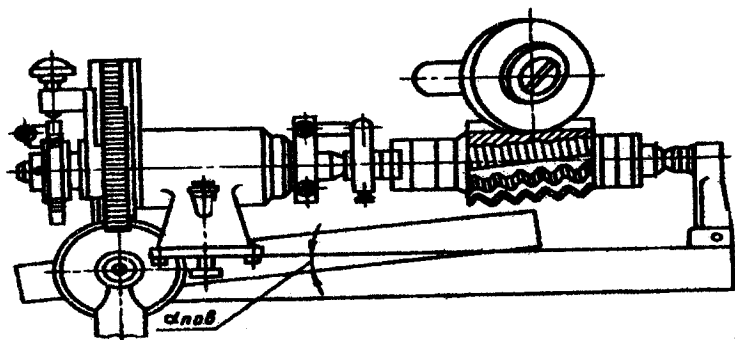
Пристрій для заточування черв'ячних фрез
